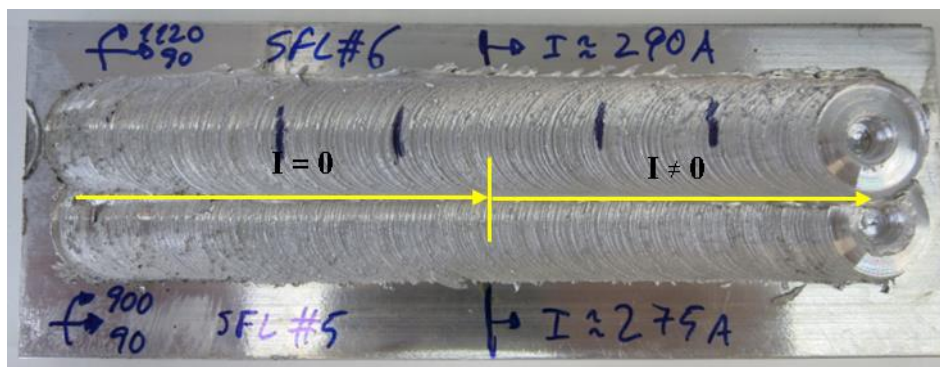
Esquema de troços de soldadura com duas zonas
